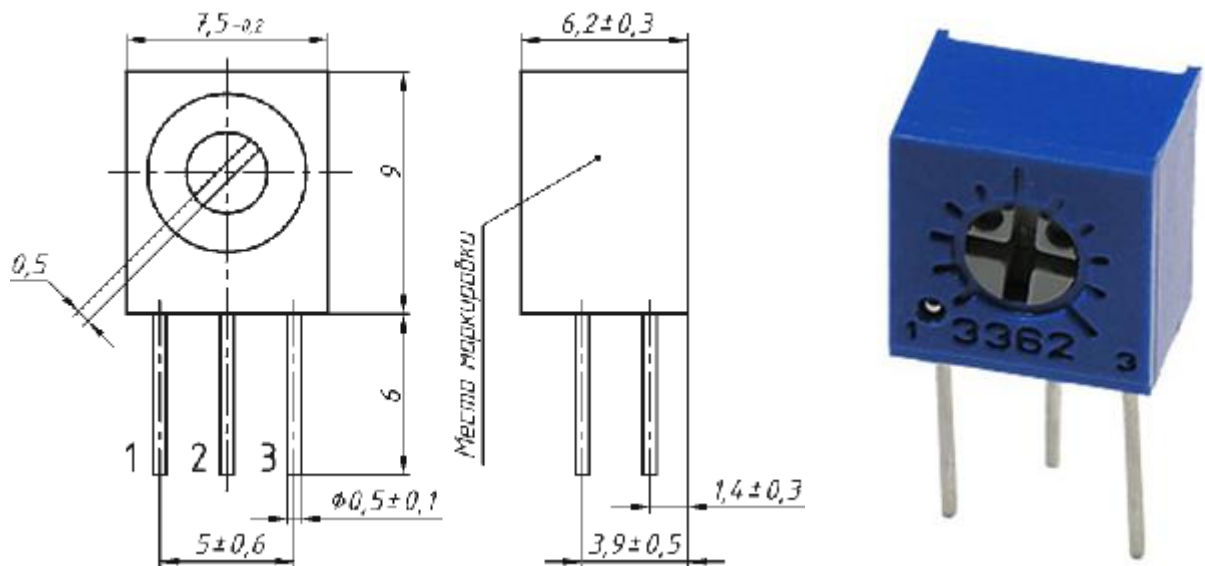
Габаритні розміри змінного резистора типу 3362S
